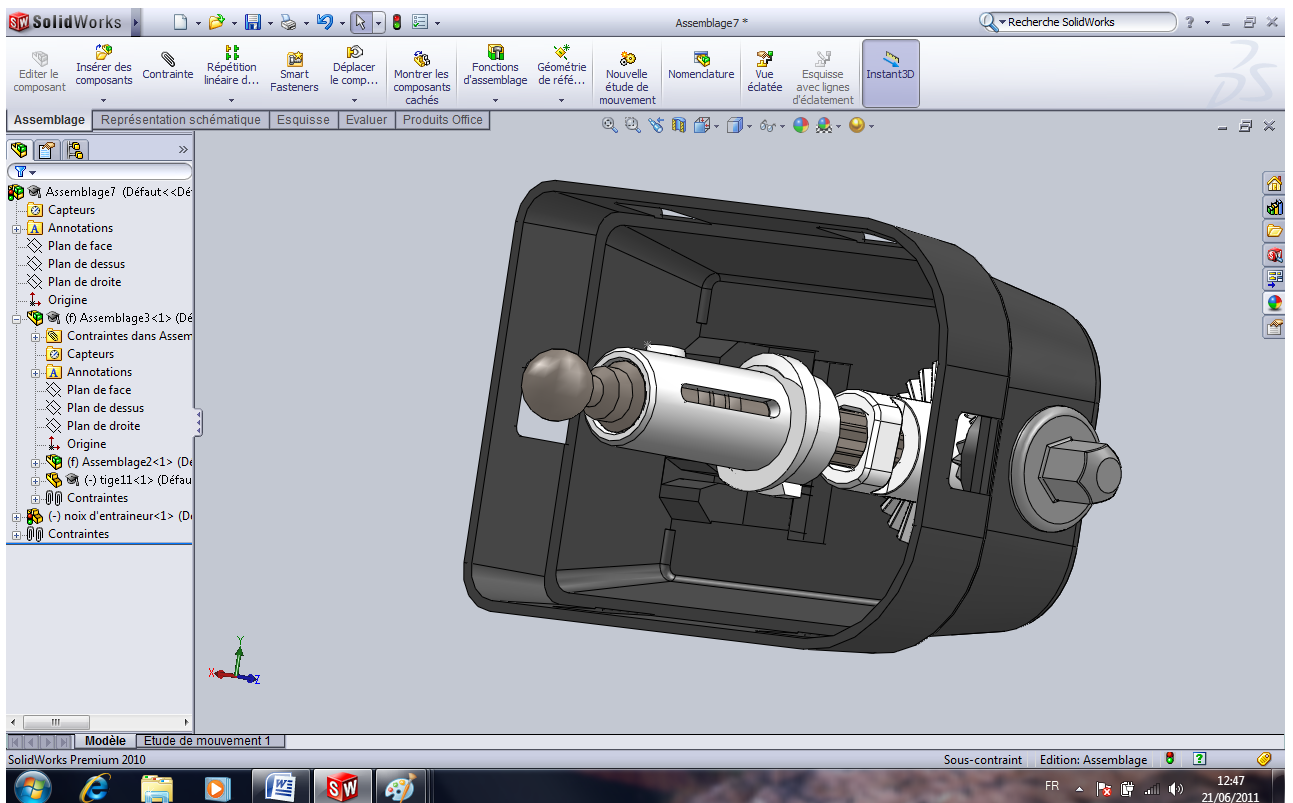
Assemblage 4(assemblage 3+manchon fileté)
